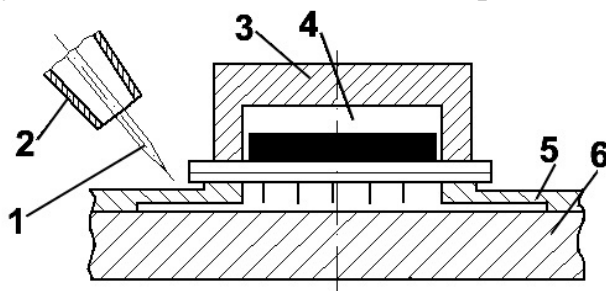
Схема аргонно–дуговой сварки
